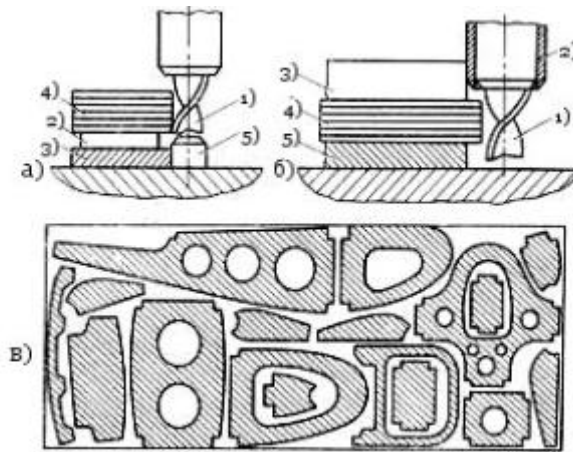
Вырезка заготовок и деталей фрезерованием:
